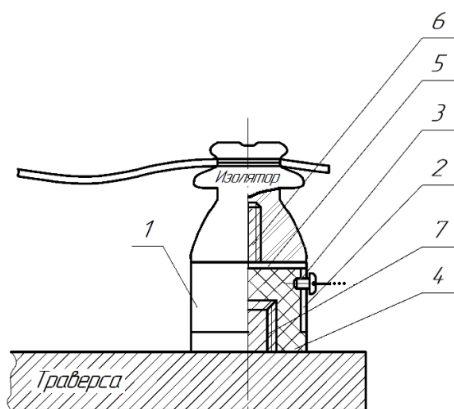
Шунт для диагностики опорных и штырьвых изоляторов (1 – шунт, 2 – полый металлический цилиндр, 3 – контакт диагностического устройства, 4 – резистивный материал, 5 – металлическая крышка, 6 – болт, 7 – втулка)
